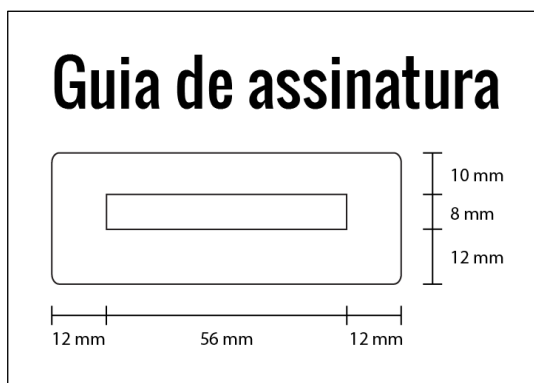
Desenho técnico da guia de assinatura (fonte: a autora)
